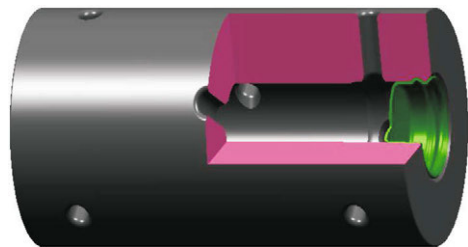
Kolbenbolzen mit Ölbohrungen und Verschlußdeckel (eingewalzt)
